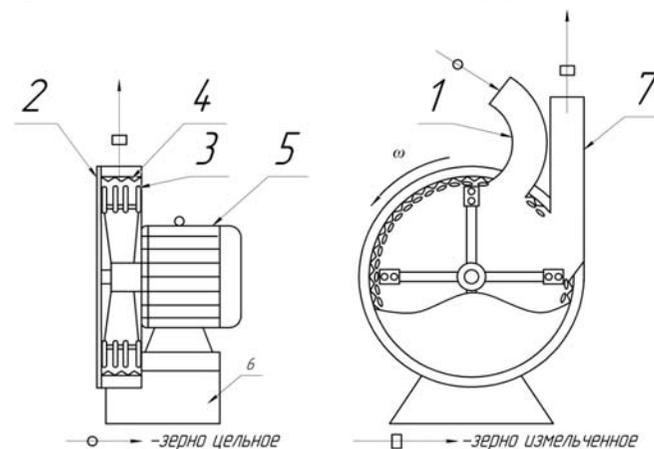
Схема модернизированной дробилки: 1 – всасывающий патрубок с металло-камнеуловителем; 2 – дробильная камера; 3 – дробильный барабан с шарнирно-подвешенными молотками; 4 – деки; 5 электродвигатель; 6 – рама; 7 – нагнетательный патрубок
